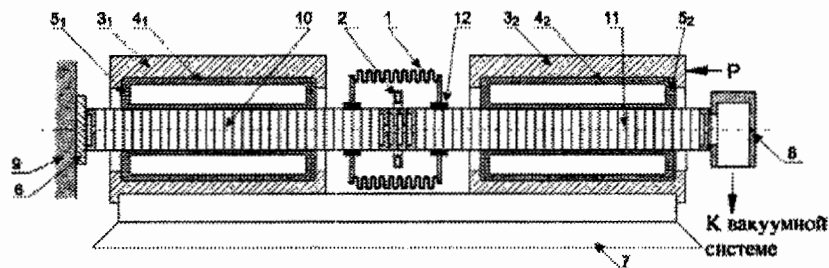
Схема установки для диффузионной сварки длинномерных изделий:
